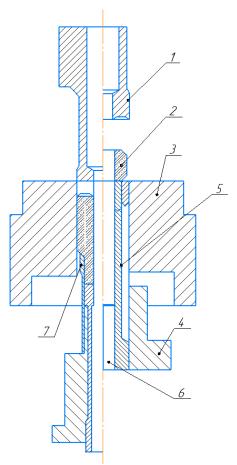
Пресс-форма с дополнительным дренирующим зазором: 1 — верхний пуансон; 2 — пористый подшипник; 3 — матрица; 4 — наружный нижний пуансон; 5 — внутренний нижний пуансон; 6 — стержень; 7 — дополнительный дренирующий зазор
